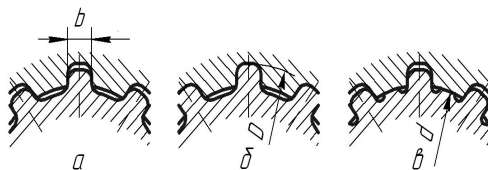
Шліцьові з'єднання з прямобічними зубцями з центруванням:
